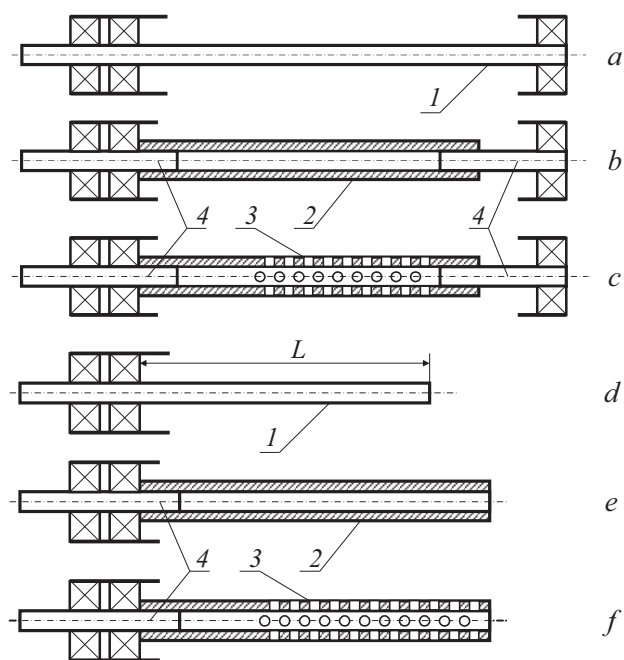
Схемы крепления сердечника в вихревом устройстве: 1 — цилиндрический сердечник, 2 — трубчатый гладкий сердечник, 3 — трубчатый перфорированный сердечник, 4 — ось.
